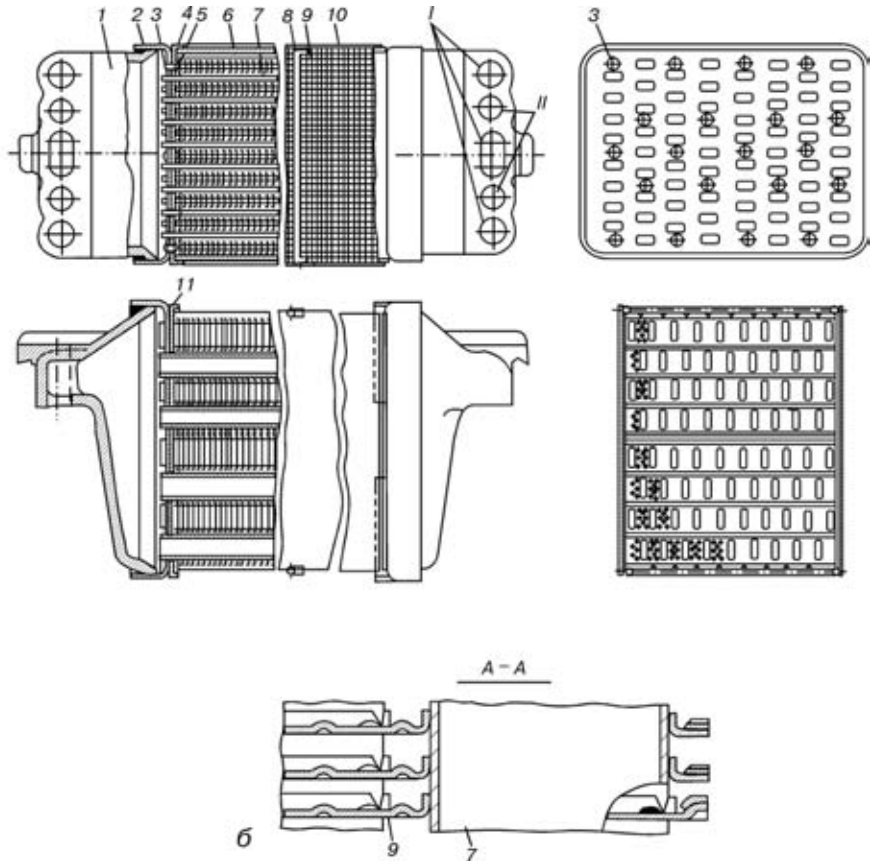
Внешний вид (а) и схема сечения водяного радиатора (б): 1 — коллектор; 2 — трубная коробка; 3 — заклепка; 4 — усиливающая доска; 5 — концевая пластина; 6 — полоса; 7 — охлаждающая трубка; 8 — пруток; 9 — охлаждающая пластина; 10 — боковой щиток; 11 — ободок; I, II — отверстия соответственно для прохода воды и крепления шпилек сечения к коллектору холодильной камеры
